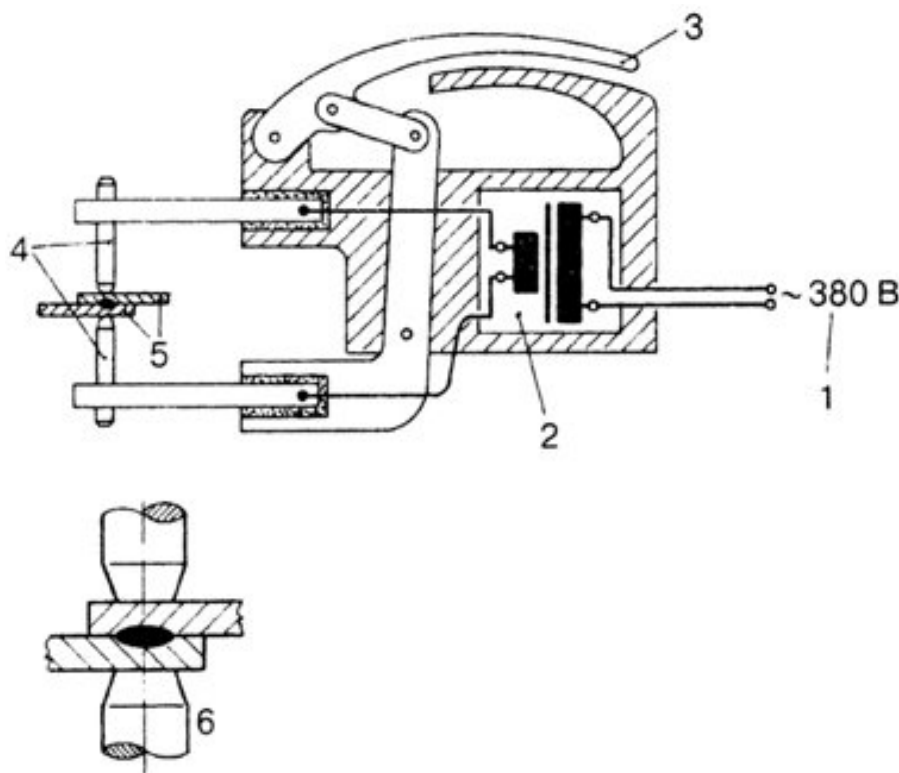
Принципиальное схематическое изображение клещей для контактно-точечной сварки и сварной точки:
